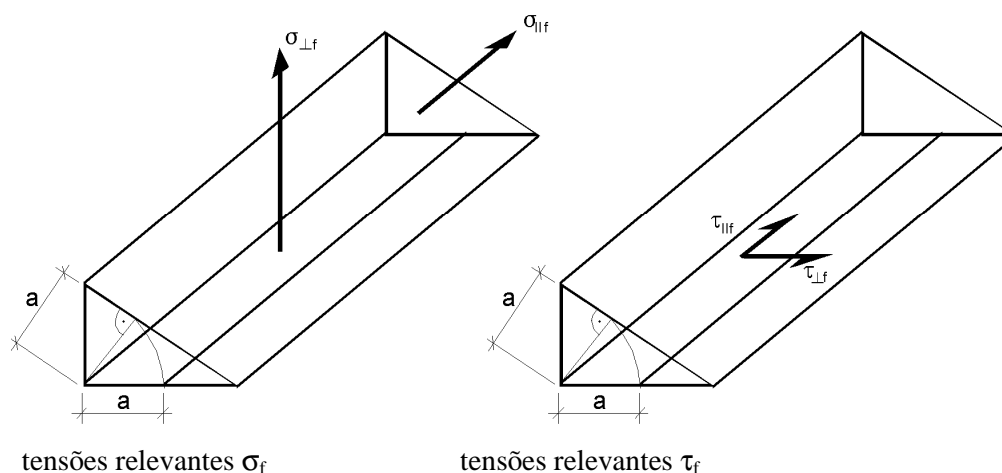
Tensões relevantes nas soldaduras de ângulo
